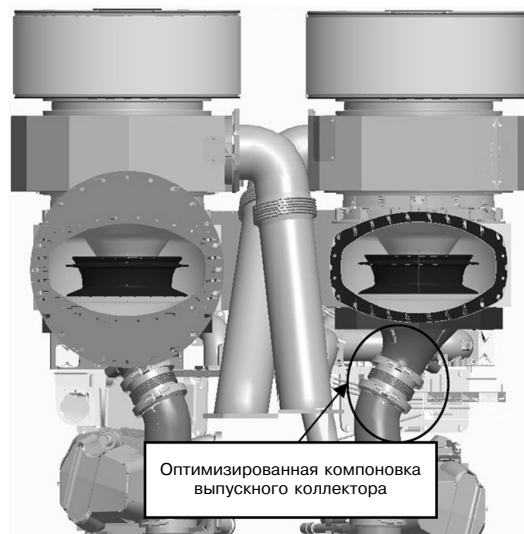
Компактная установка двух турбокомпрессоров на двигателе
